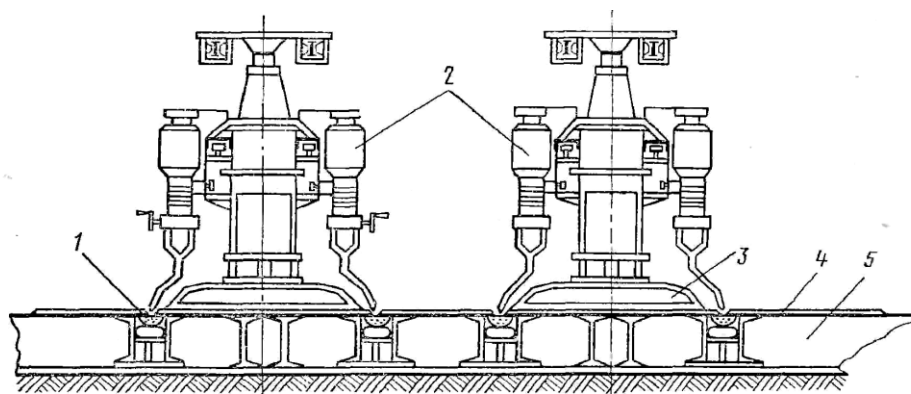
Стенд для автоматической сварки листов цилиндрической части котла цистерны:
